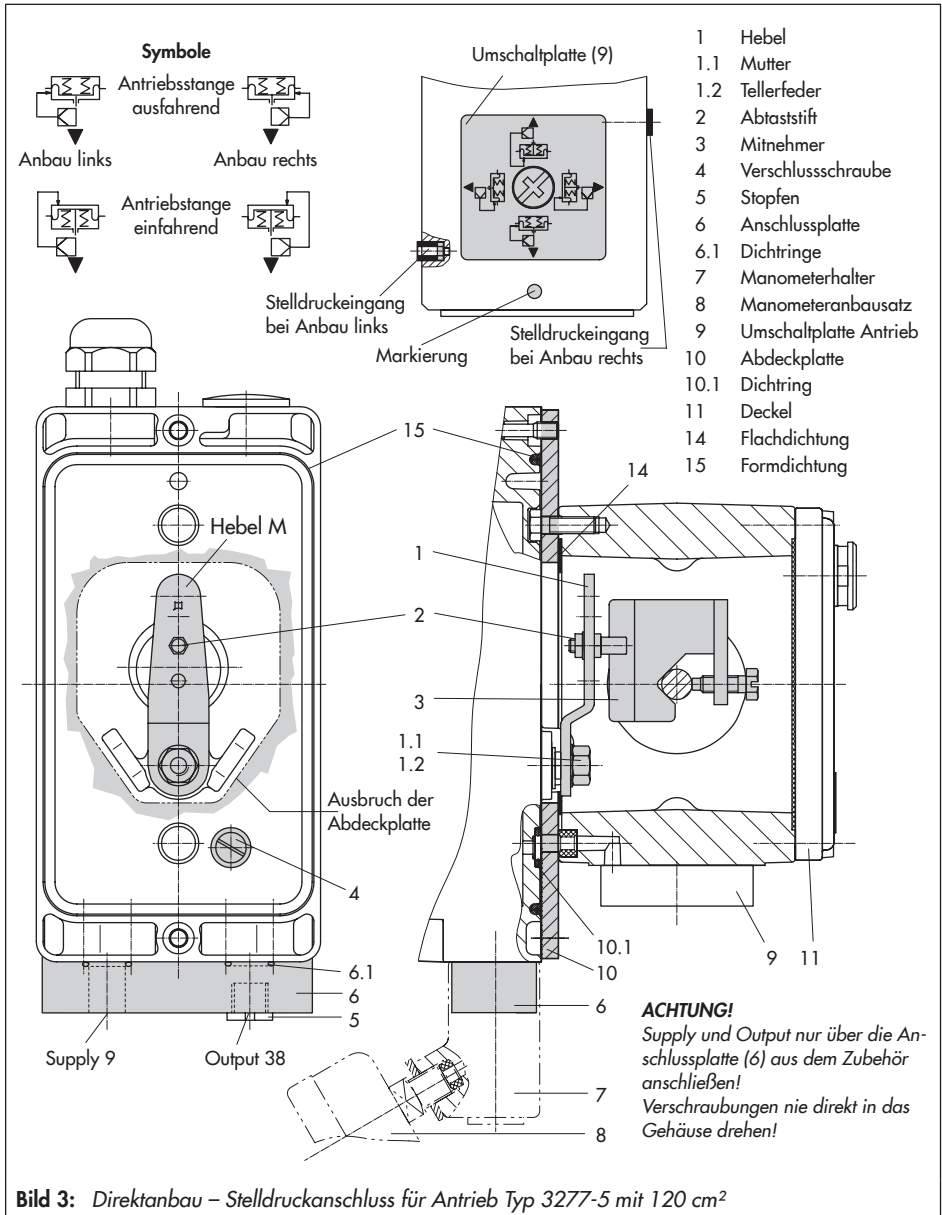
Direktanbau – Stelldruckanschluss für Antrieb Typ 3277-5 mit 120 cm²
